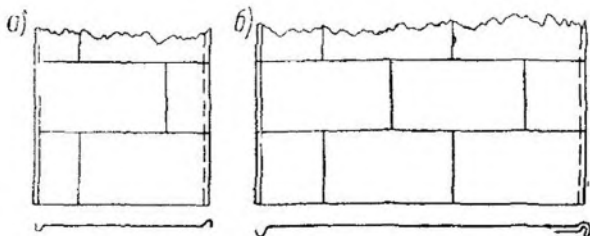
Изготовление картин для воздуховодов большого диаметра
